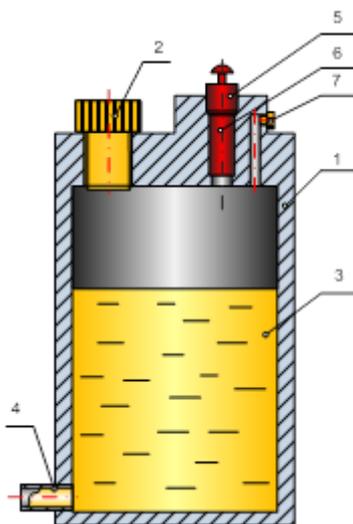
Конструкция пирогенератора давления: 1 — корпус; 2 — пробка; 3 — рабочая жидкость; 4 — штуцер; 5 — затвор; 6 — пиропатрон; 7 — предохранительный клапан
